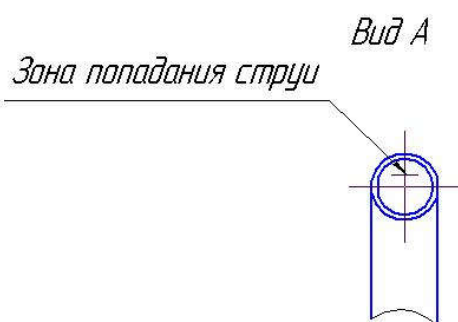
Схема регулировки элементов цилиндрической печатающей головки
